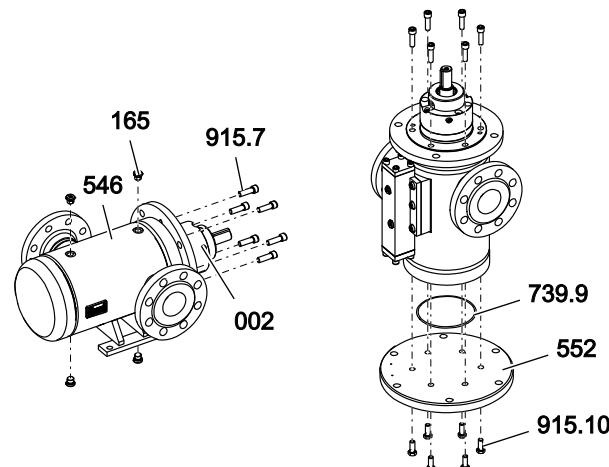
Pièces de rechange boîtier extérieur acier – Image de principe
